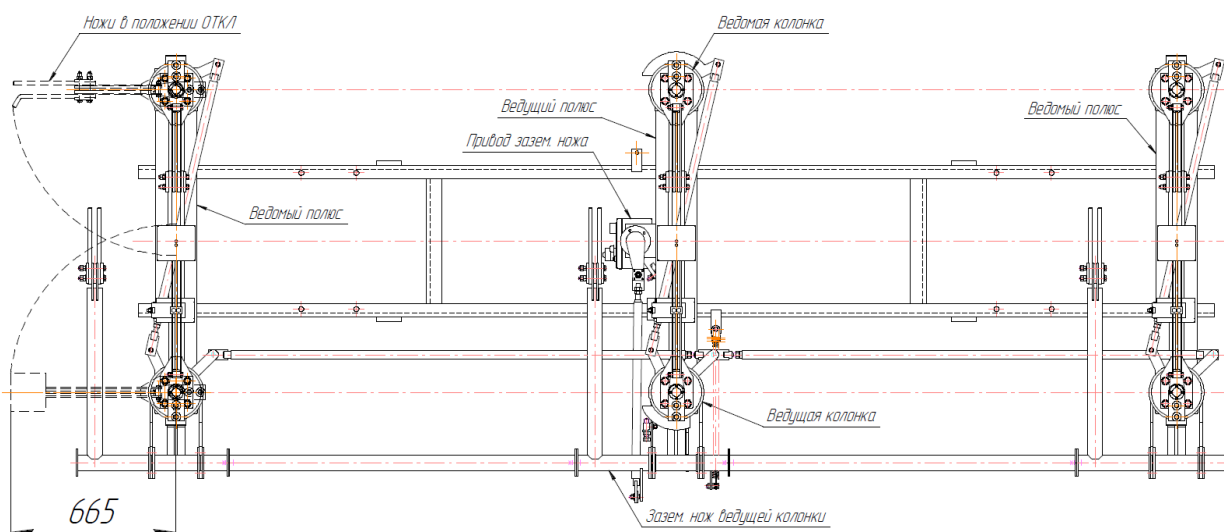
Разъединитель РГП-СЭЦ-110/1250 УХЛ1. Вид сверху
